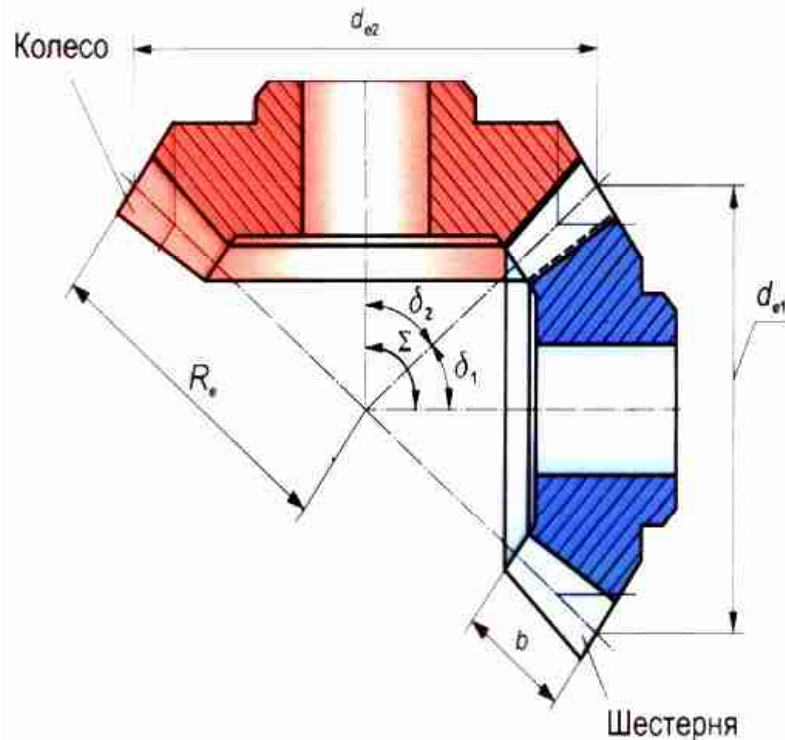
Конические зубчатые колеса в зацеплении
